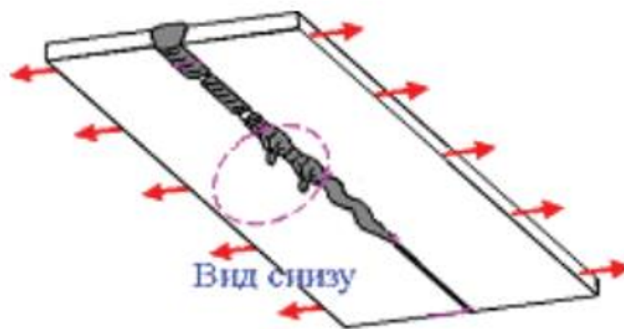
Эскиз дефекта сварного шва
